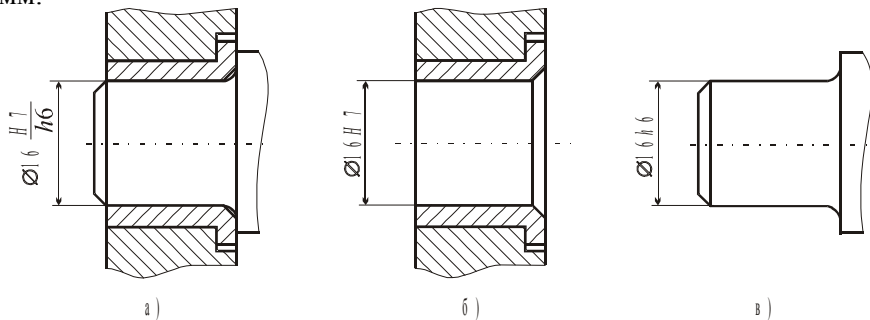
Схема соединения с обозначением посадки и деталей с обозначением полей допуска
